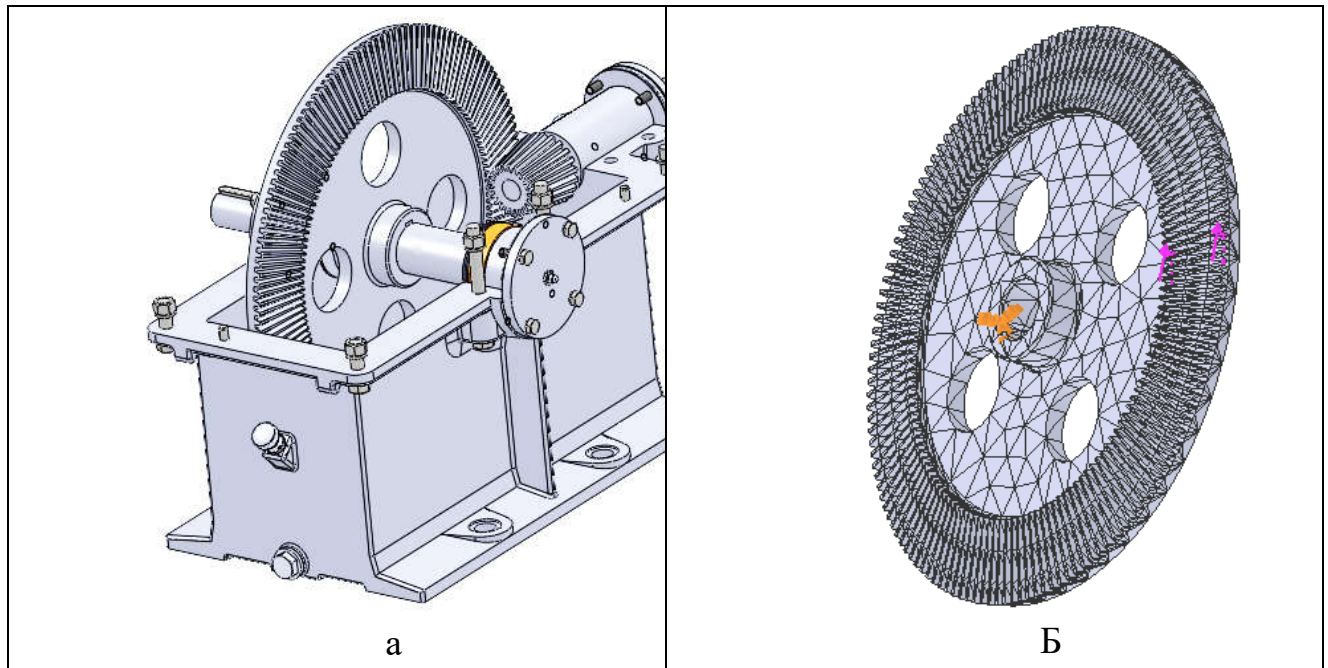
Твердотільна модель редуктора (а) і скінченно-елементна модель конічного колеса
